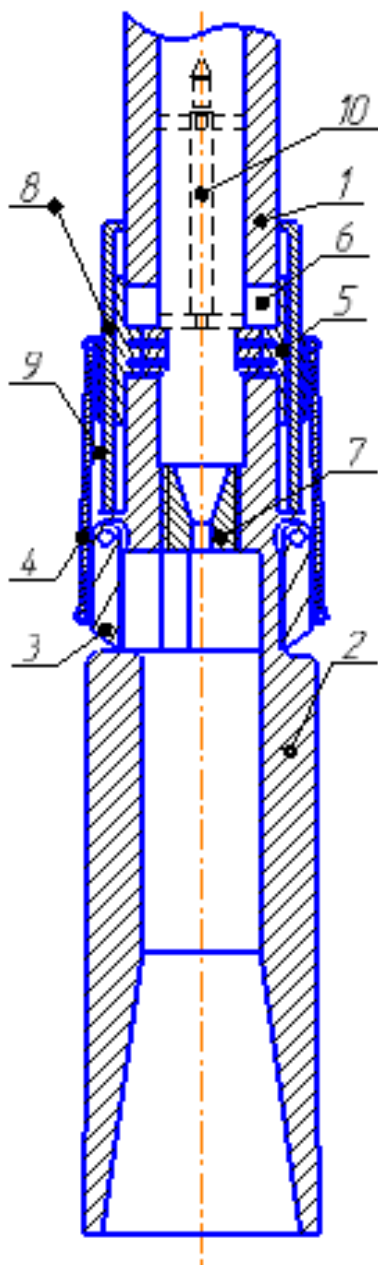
ЗУ с механизмом шарнирно-рычажного типа:
